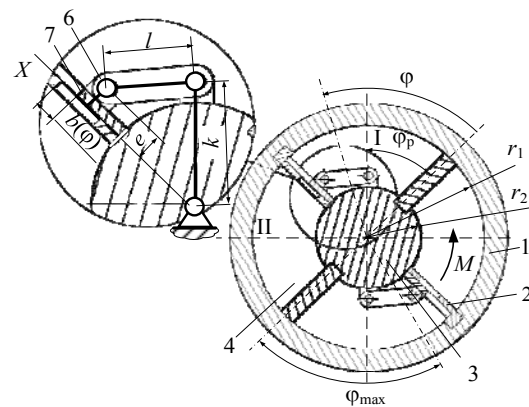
Розрахункова схема запропонованого важільно-лопатєвого амортизатора
